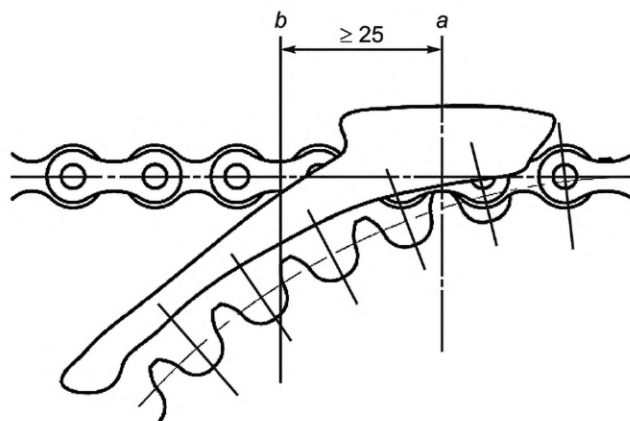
Требования к защитному устройству цепи и приводного ремня (минимальные)
